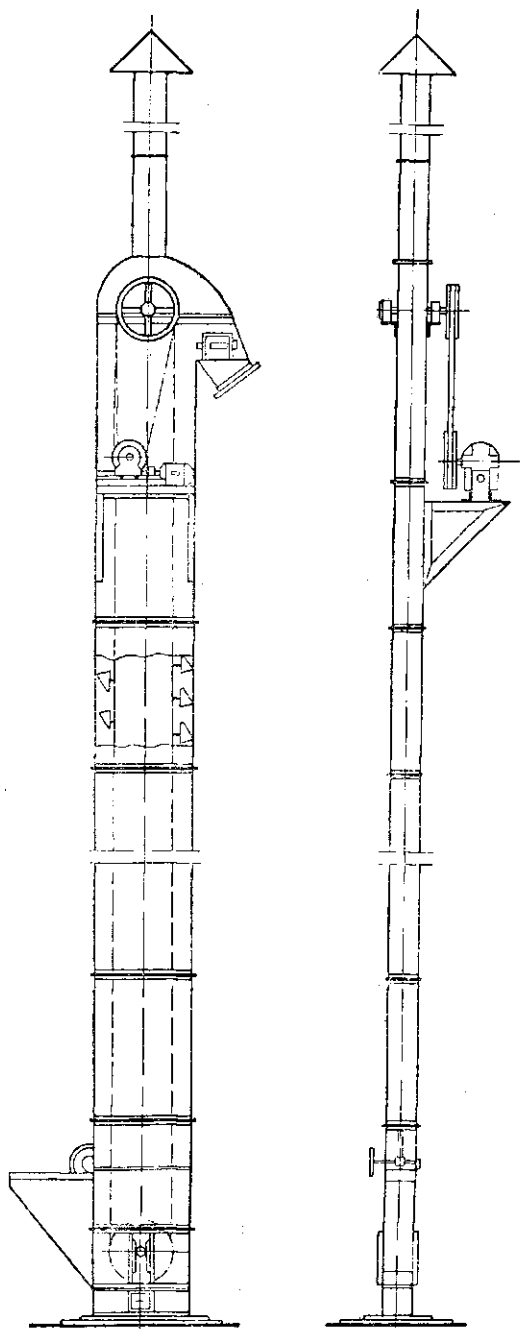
Вертикальный шнековый элеватор ПВ-4.
